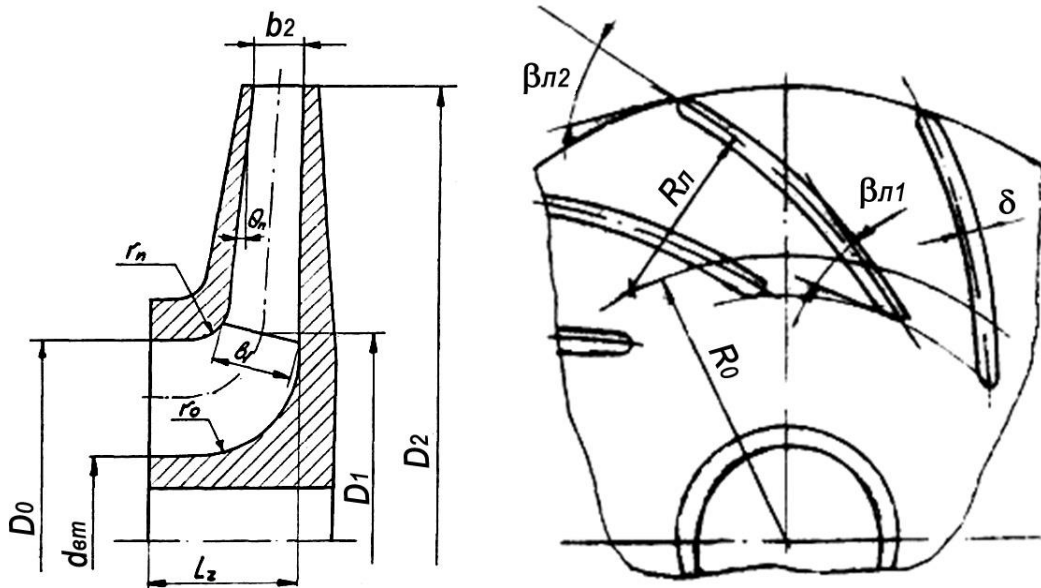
Схема та основні розміри робочого колеса з циліндричними лопатками
